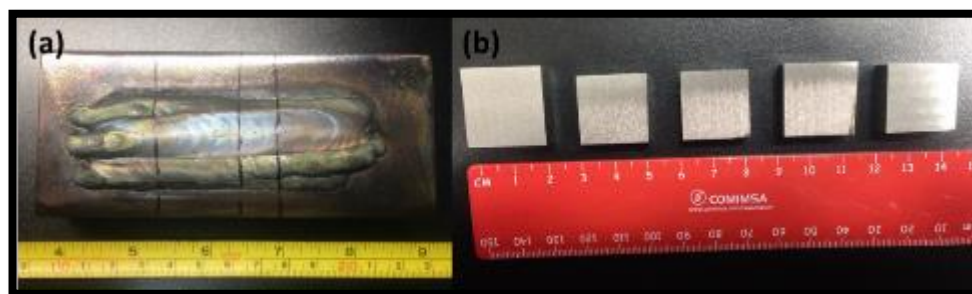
(a) Probeta de soldadura de 12 x 5 cm y (b) cupones de 2 x 2 cm para ensayo de desgaste.
